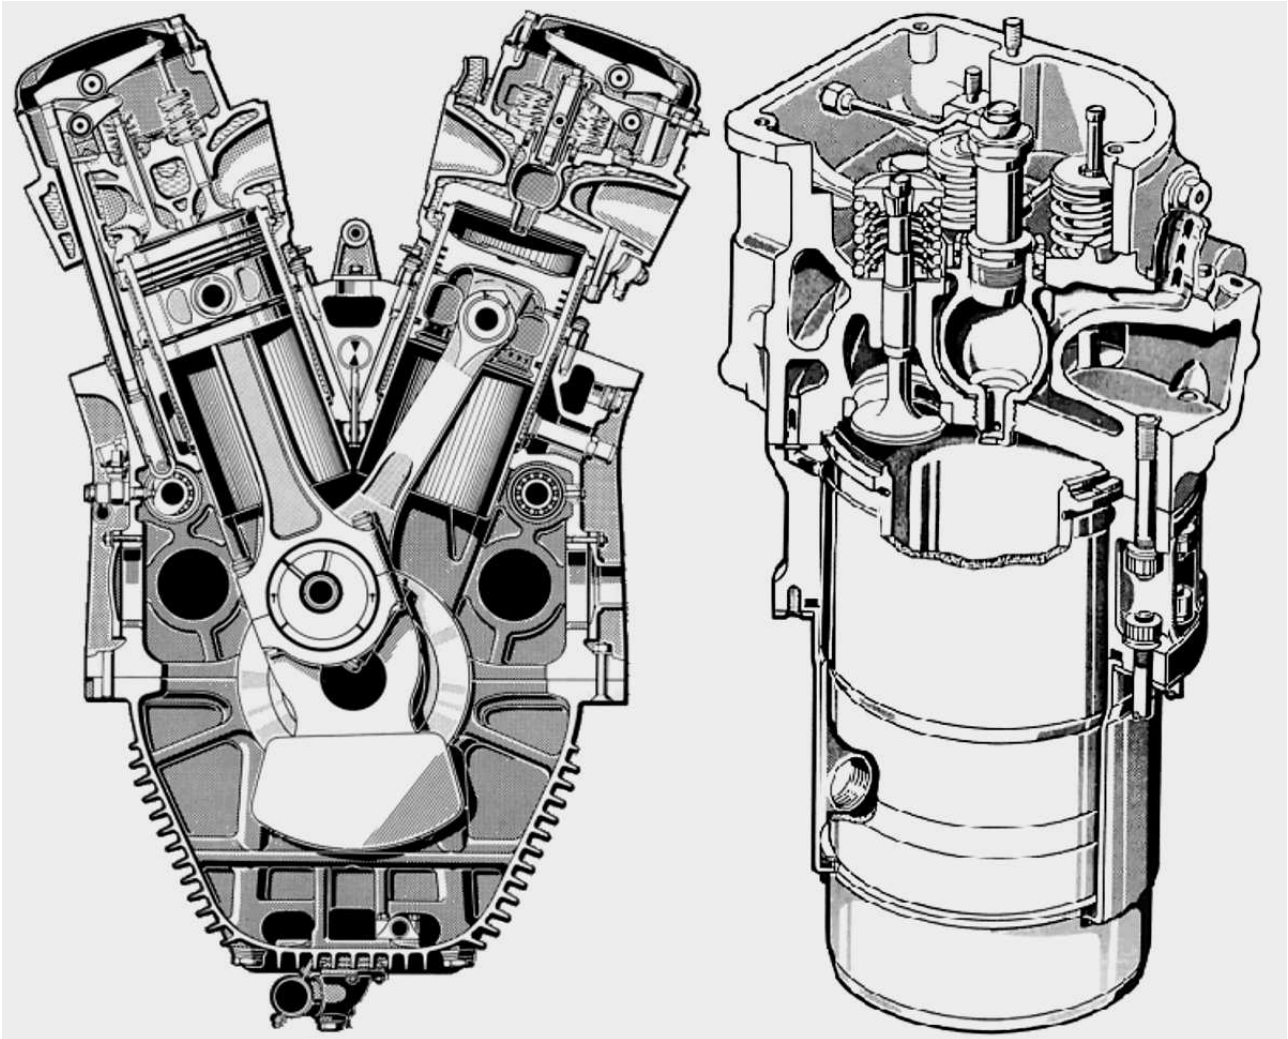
sezione trasversale di un motore MB518 ed assonometria di un cilindro dello stesso motore; il disegno ed i componenti dei motori MB 501 e MB 511 erano molto simili; motori V-20 a 40 gradi con cilindri separati collegati solo dal carter. Si notano la camera pre-combustione, il gruppo valvole ed i due alberi a camme.
